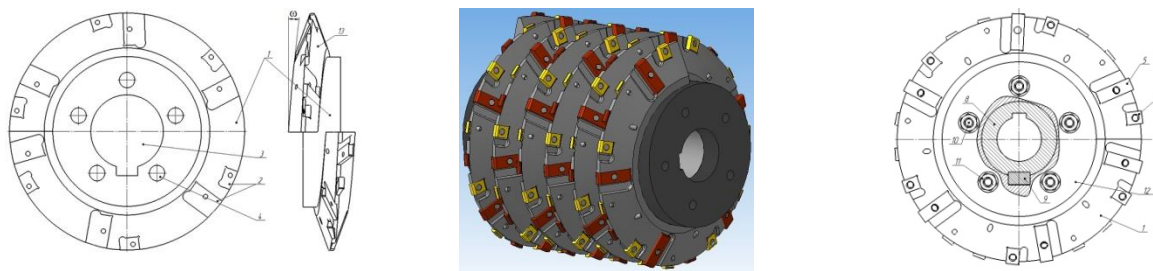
Конструкция сборной червячной фрезы с СРТП
